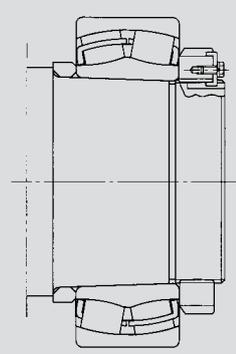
Конический вал, стопорный бугель (с дистанционным кольцом)
